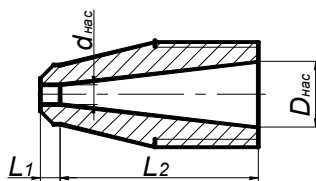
Схема конідального насадка з круглим вихідним отвором:
